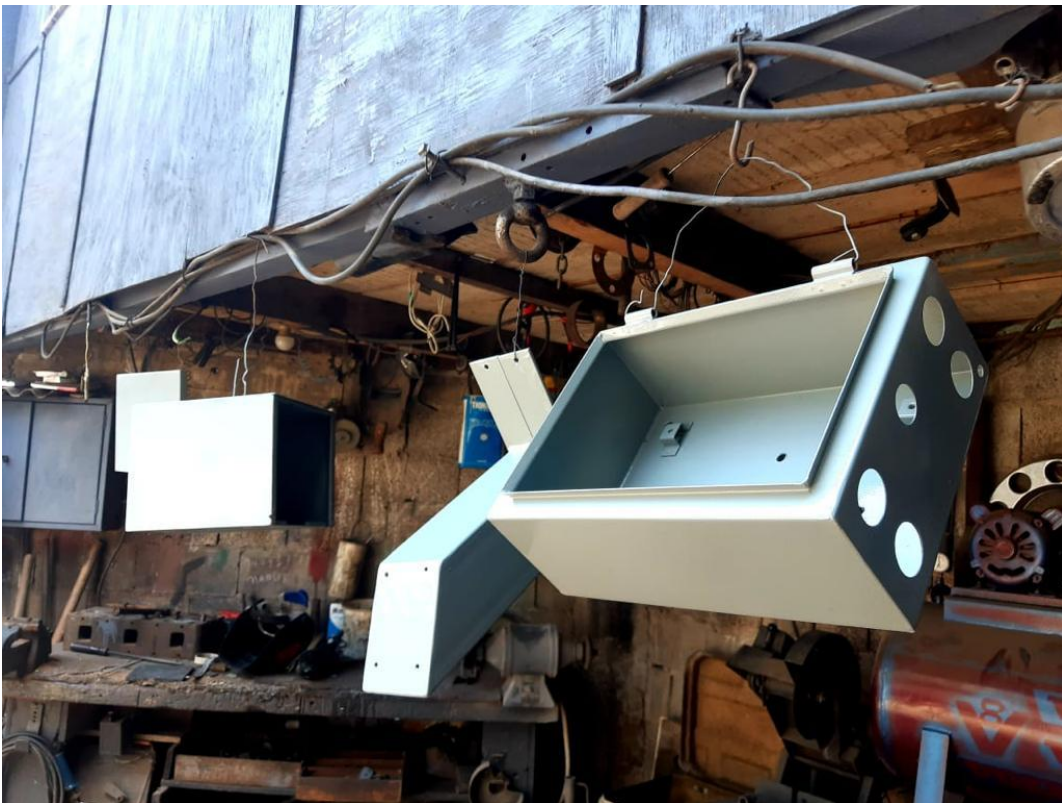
e 26 – Ressecamento da pintura das estruturas do CLP.
